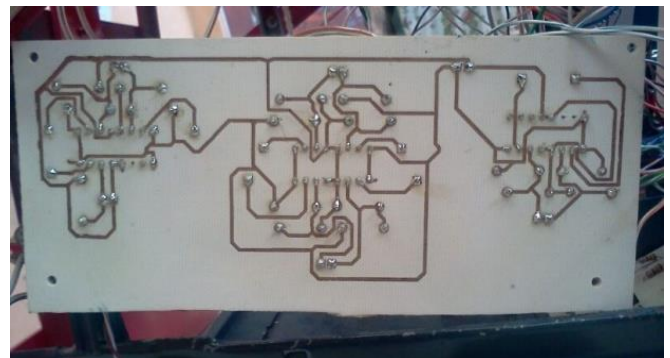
Fotografía de la parte frontal de la placa de los drivers
